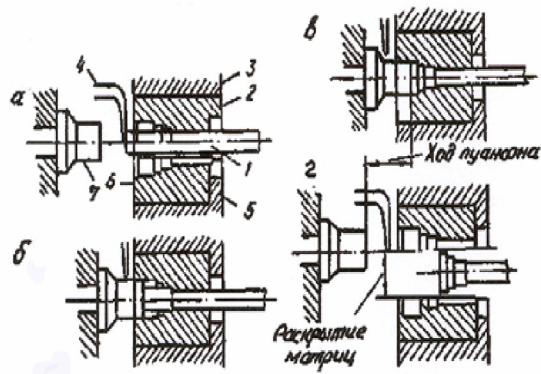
Процесс штамповки на горизонтально – ковочной машине
